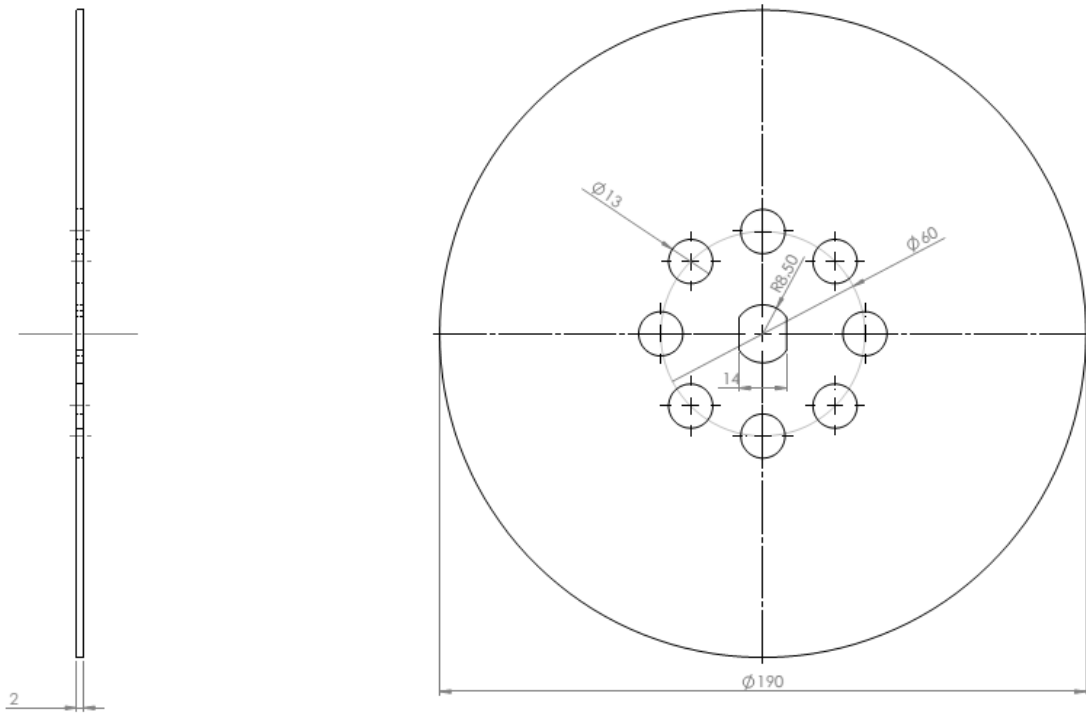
Dimensões (em milímetros) dos discos do rotor tipo I.
